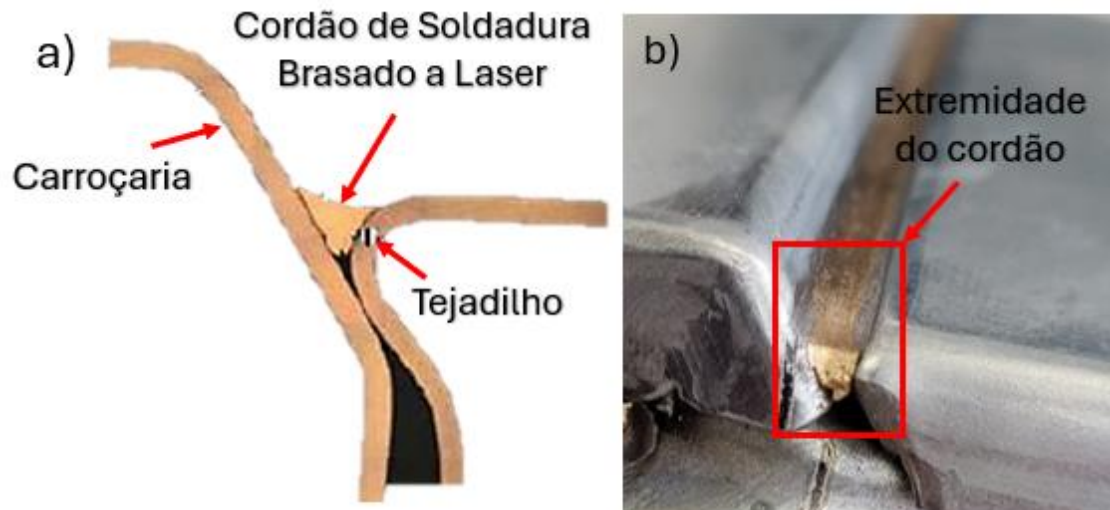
Cordão de Soldadura por Brasagem a Laser, adaptado de [49]
